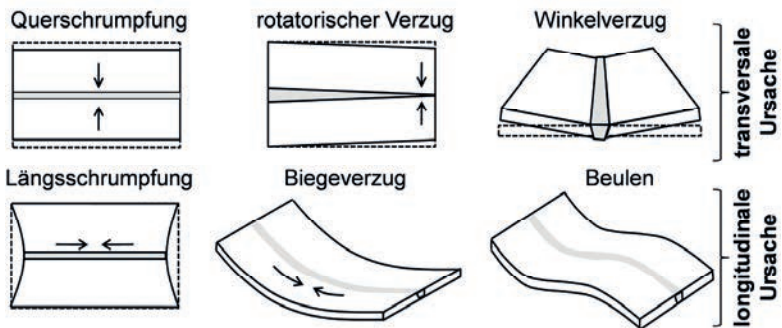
Grundlegende Verzugsformen; die Pfeile deuten die Schrumpfungsrichtungen der Schweißnähte beim Abkühlen an [MASUBUCHI 1980; gezeichnet nach SCHENK 2011, S. 34]
